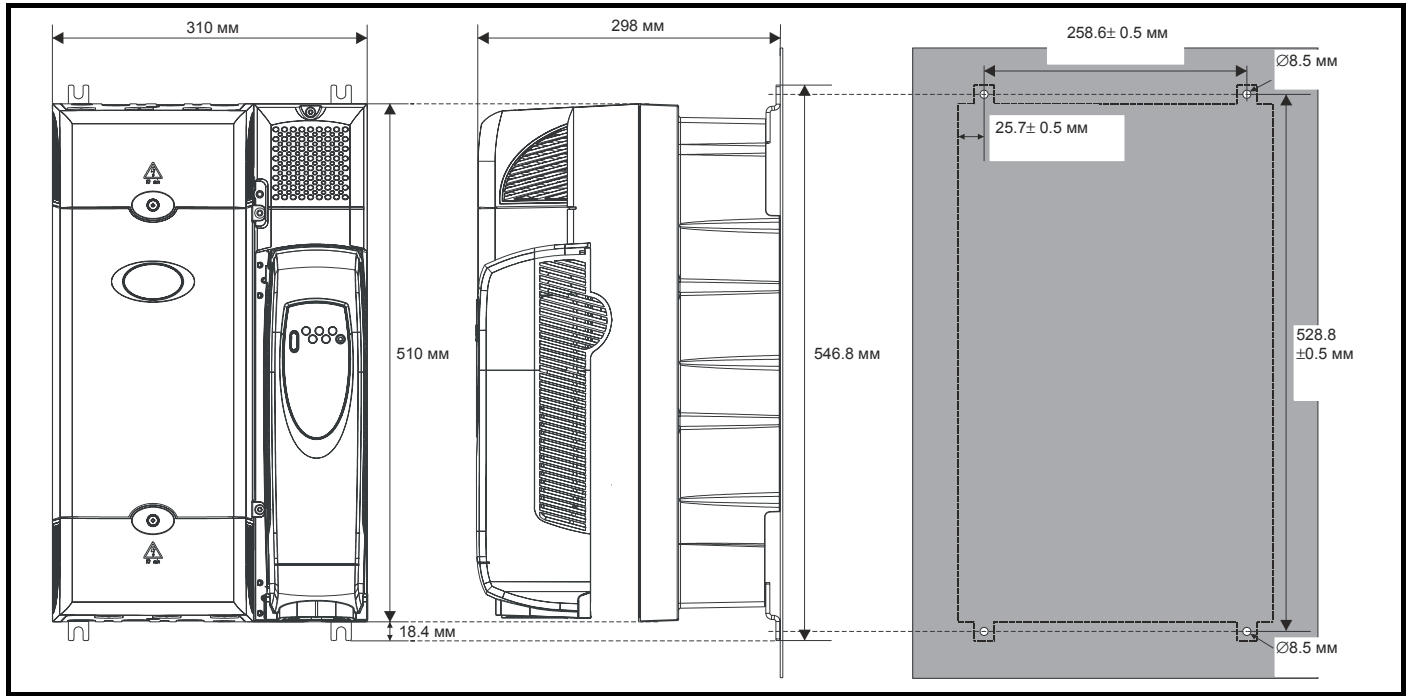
Монтаж к поверхности для привода габарита 5
